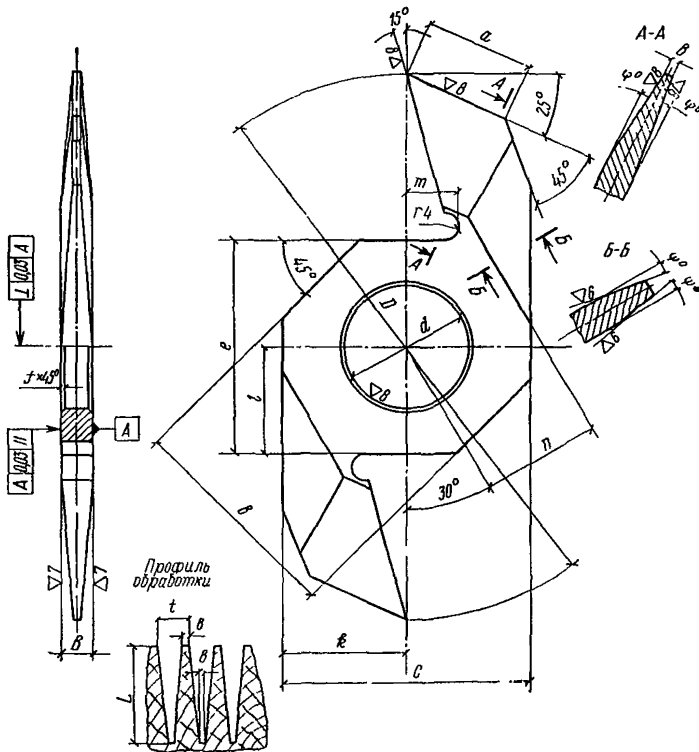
Режущий инструмент для фрезерования зубчатых шипов (величины габаритов и угловых размеров фрез для различных типов соединений приведены на стр. 58)
